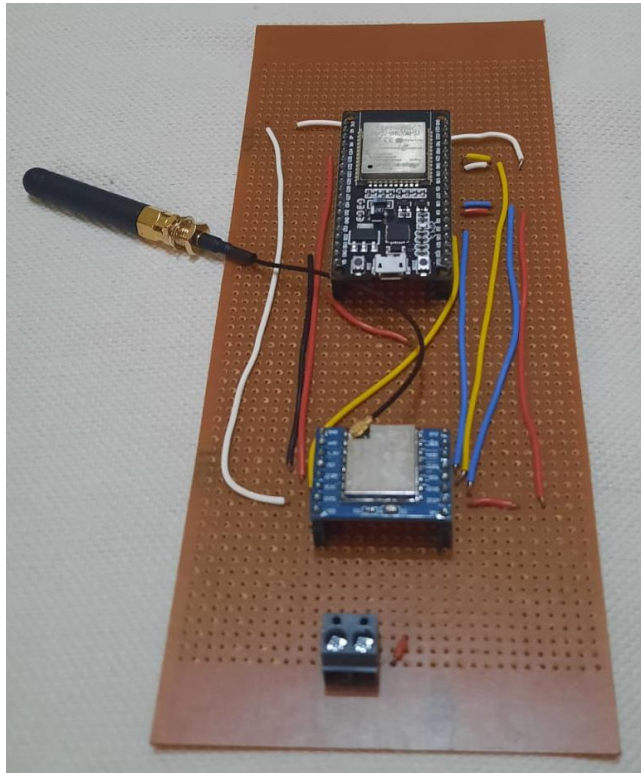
Placa superior. Cara de las soldaduras.
